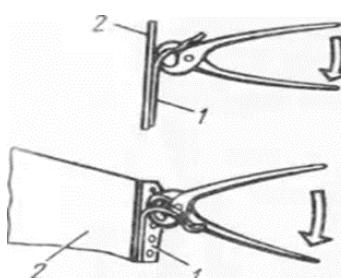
Удаление полосы точечной сварки ручным инструментом: 1 — полоса металла; 2—деталь кузова
